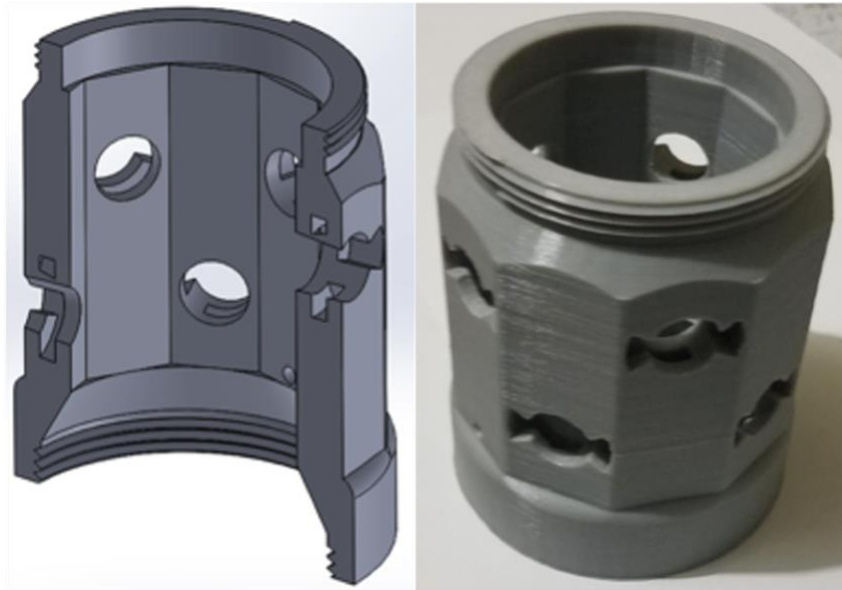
a) Detalles del interior de la torre de montaje, b) Impresión 3D de la torre base de montaje
